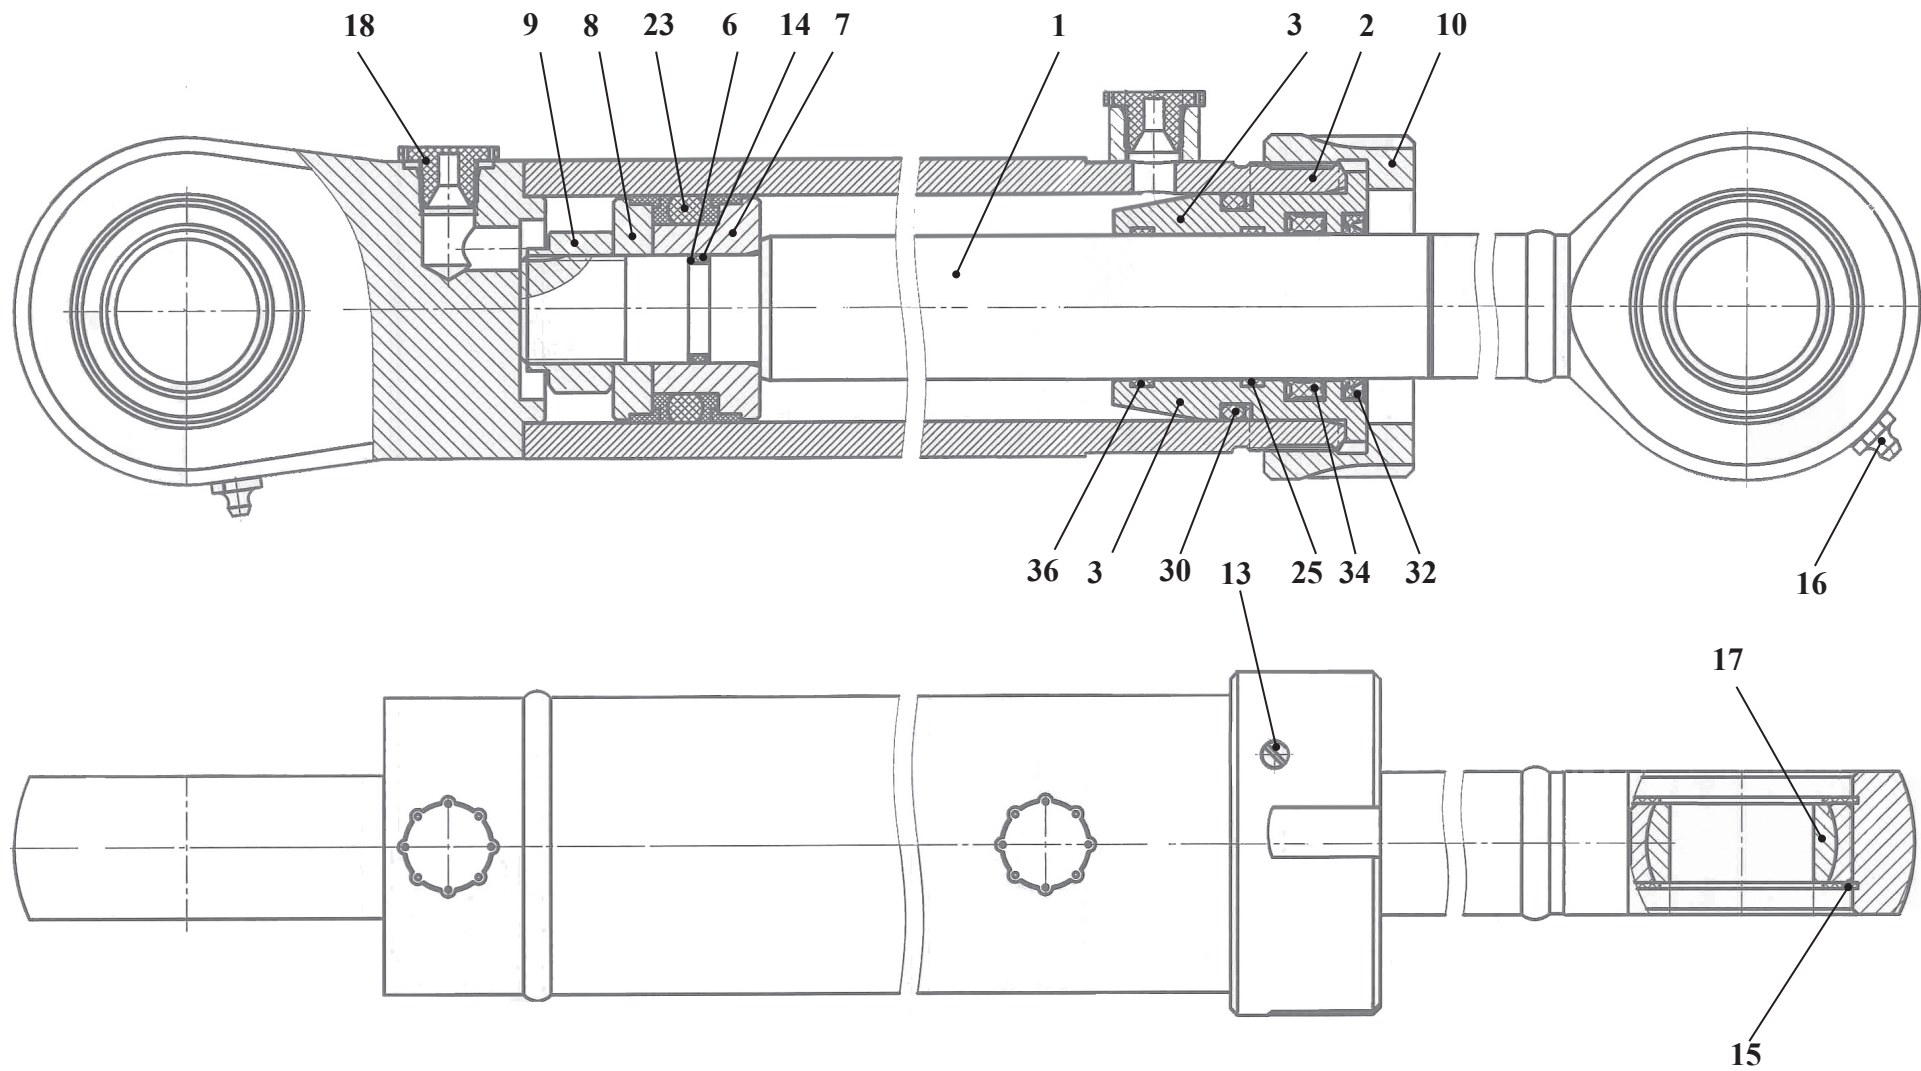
ЦГ-63.40x400.765.11.000	Гидроцилиндр поворота руля
